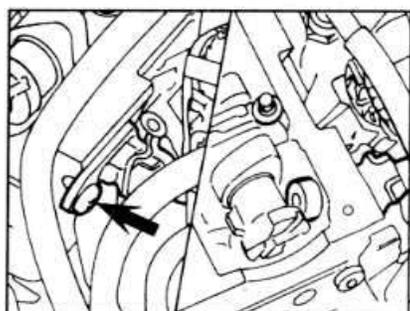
D.17. Расположение датчика положения распределительного вала в головке блока цилиндров.
